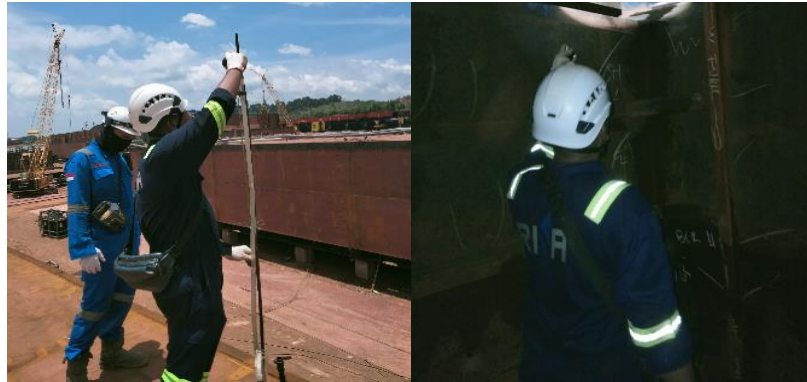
151. *Visual Weld Inspection T.Bulkhead
